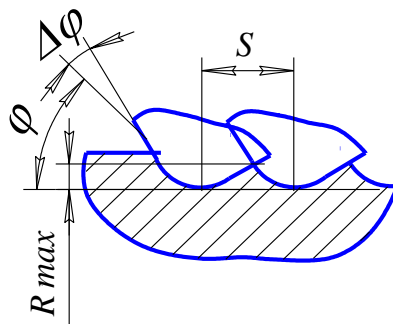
Похибка розташування радіусної калібруючої кромки
